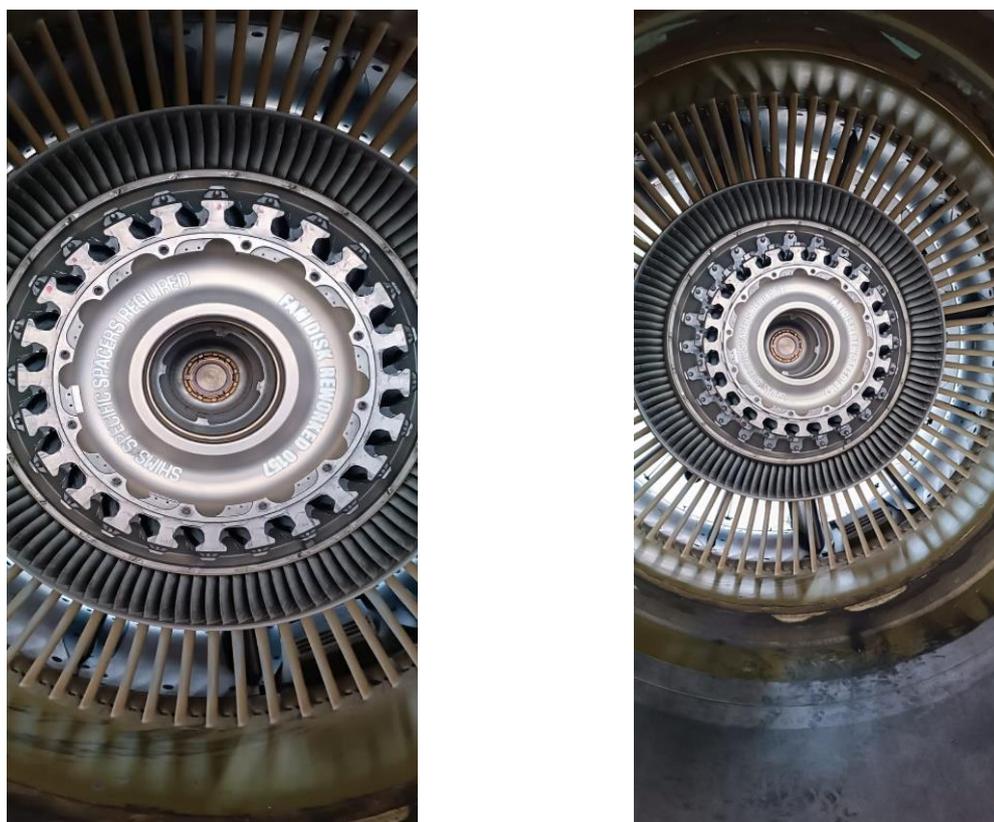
Vista do motor depois de removidas as fan blades e platforms. Fonte: (Autor).
